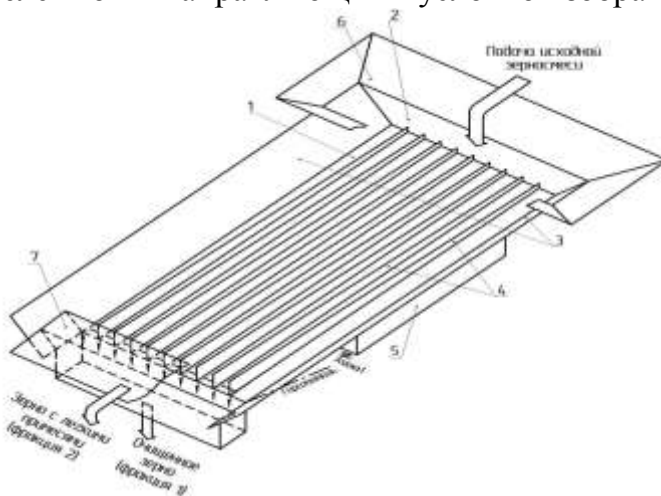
Схема рабочего органа: 1- рабочий орган; 2-торцевая стенка; 3- боковые стенки; 4- рифли; 5- привод; 6 - питатель; 7- нож.
